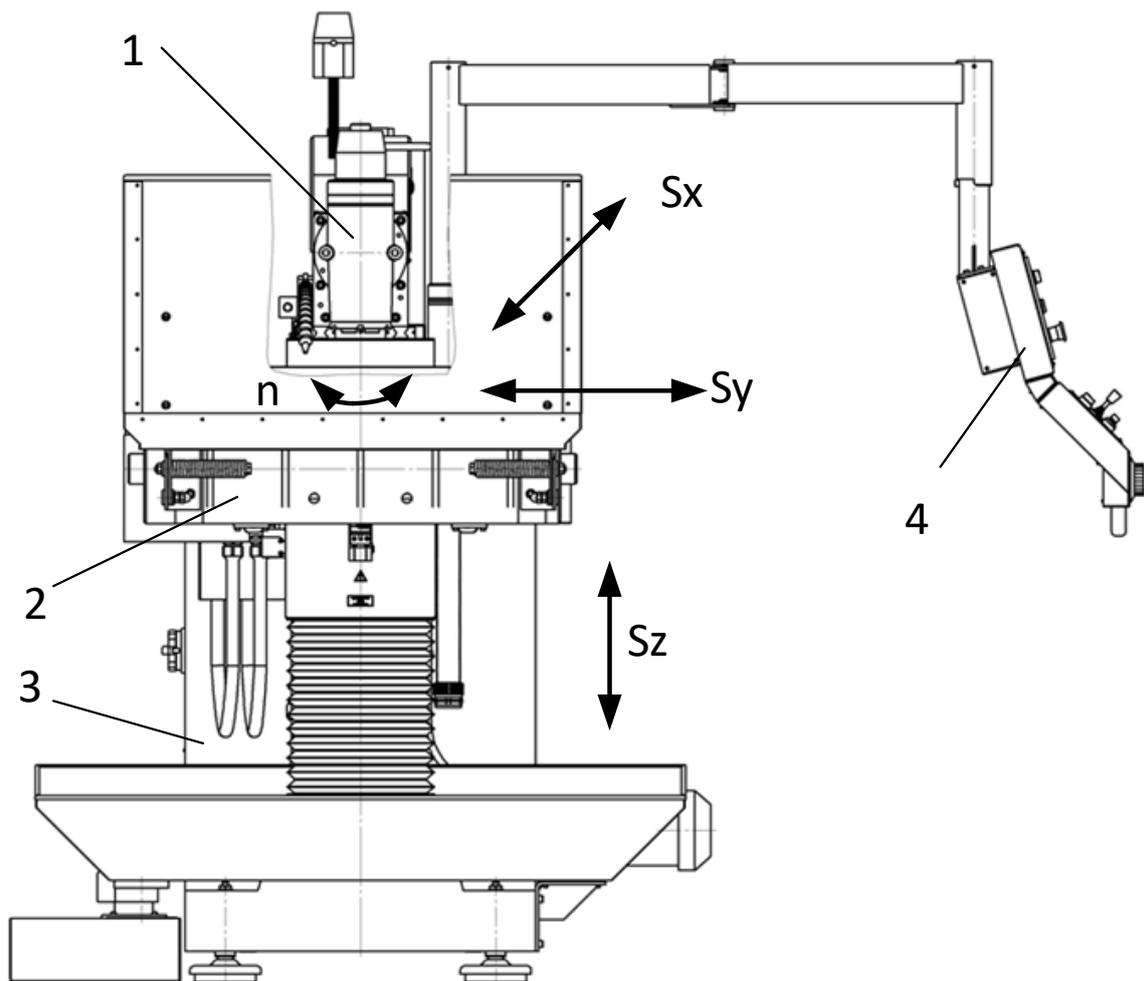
Вид вертикально фрезерного станка с ЧПУ
